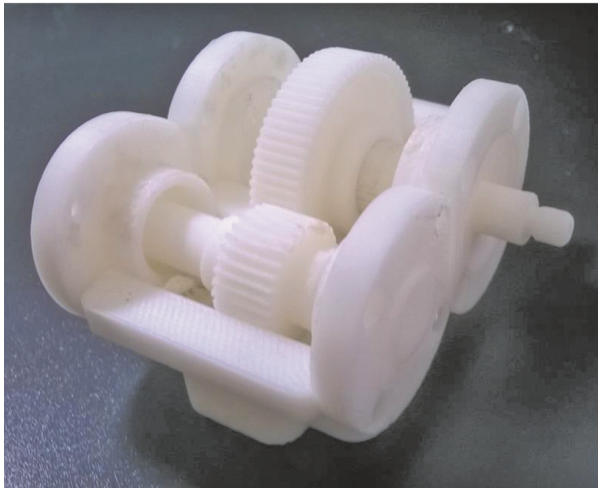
Результаты 3D-печати одноступенчатого редуктора
